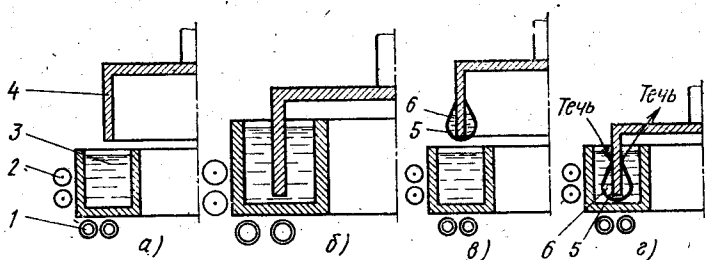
Сверхвысковакуумное разъемное соединение с расплавляемым металл-уплотнителем:
